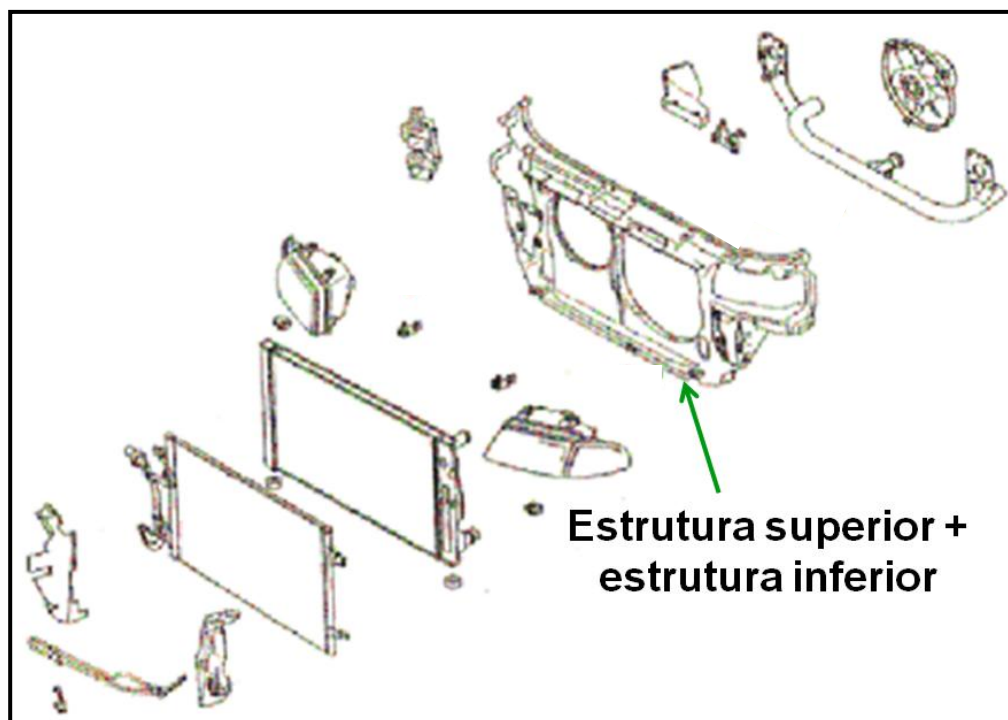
Vista explodida módulo frontal (Fonte: AUTOR).
